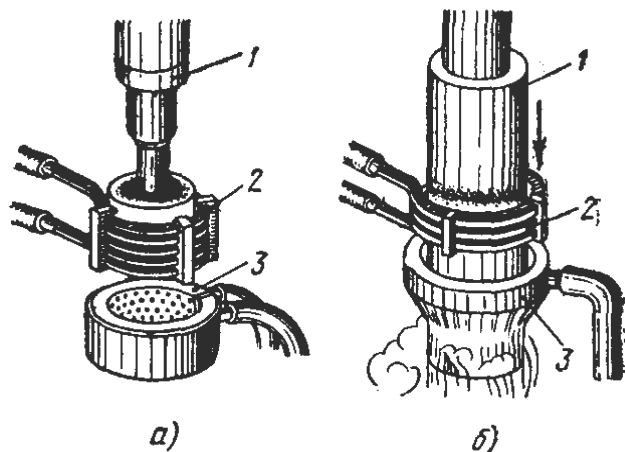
Многовитковый индуктор для закалки током радиочастоты: а – при одновременном нагреве; б – при непрерывно-последовательном нагреве
